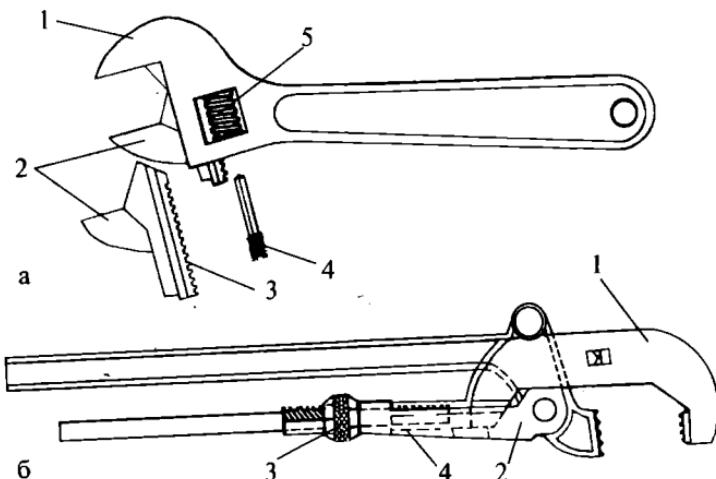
Ключи: а — разводной гаечный (1 — неподвижная губка; 2 — подвижная губка; 3 — рейка; 4 — ось; 5 — червяк); б — трубный рычажный (1 — неподвижный рычаг; 2 — подвижный рычаг; 3 — гайка; 4 — обойма)
